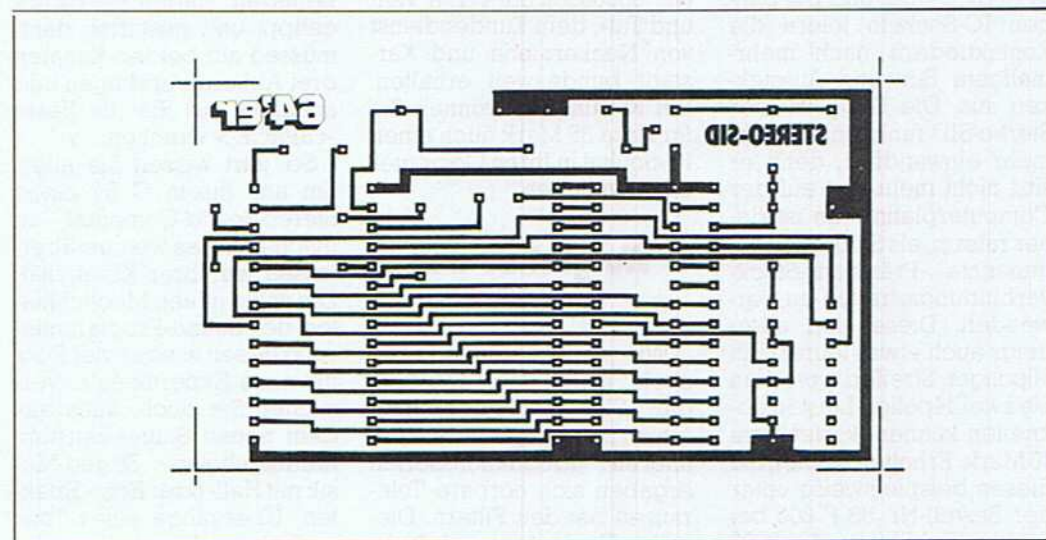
Layout für die Stereo-SID-Platine (spiegelverkehrt)
